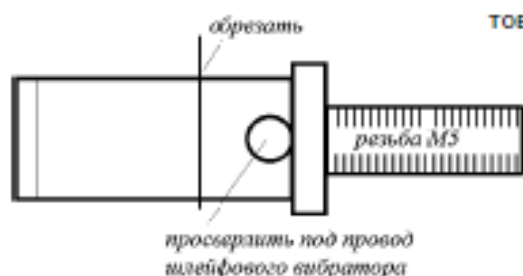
Эскиз подготовки винтов крепления активного вибратора из ножевых контактов мощного соединителя
